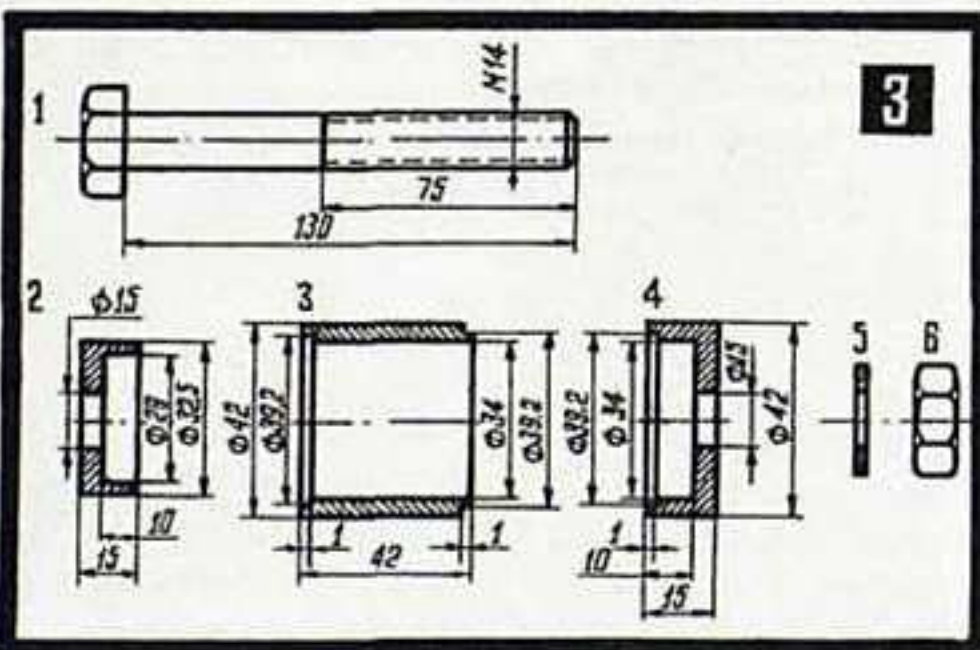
Съемник втулок для «Запорожца»: 1 — болт; 2 и 4 — фигурные шайбы; 3 — трубка; 5 — шайба; 6 — гайка.
